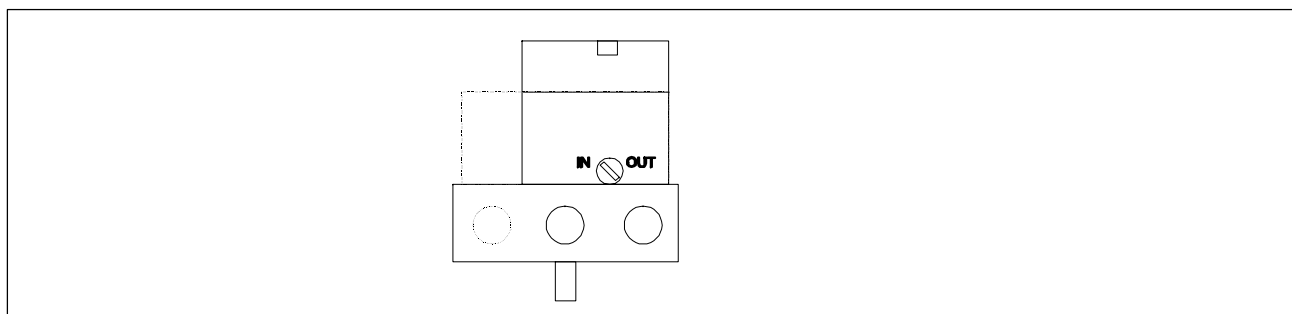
Conmutador de aire de limpieza en el bloque de válvulas, vista del posicionador del lado de conexiones neumáticas con la tapa abierta
